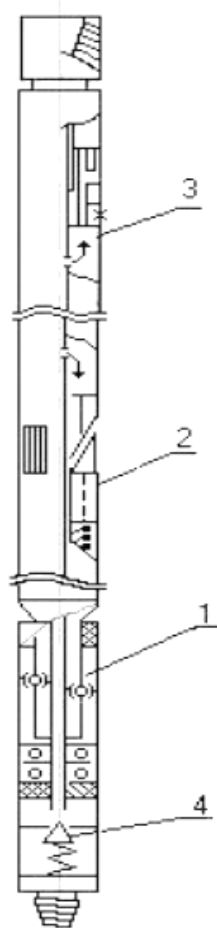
Устройство для развинчивания труб в скважине УРТ: 1 – реверсивный редуктор; 2 – якорь; 3 – механизм блокировки; 4 – плечевой клапан-дроссель
